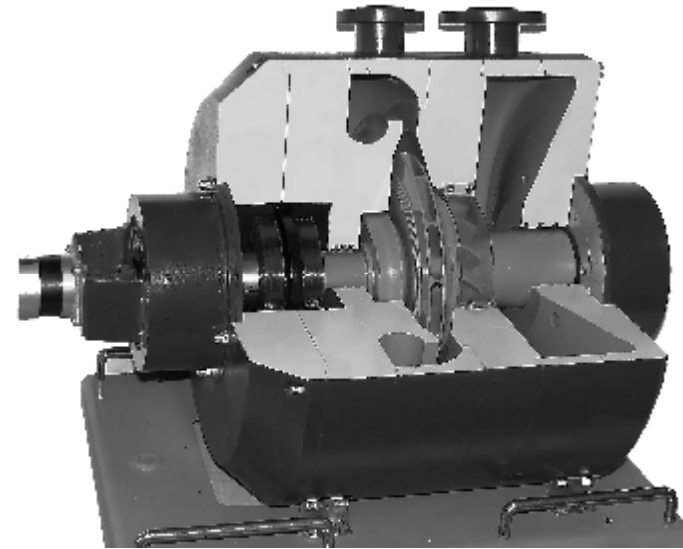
Модель компрессора ГПА с магнитными подшипниками
